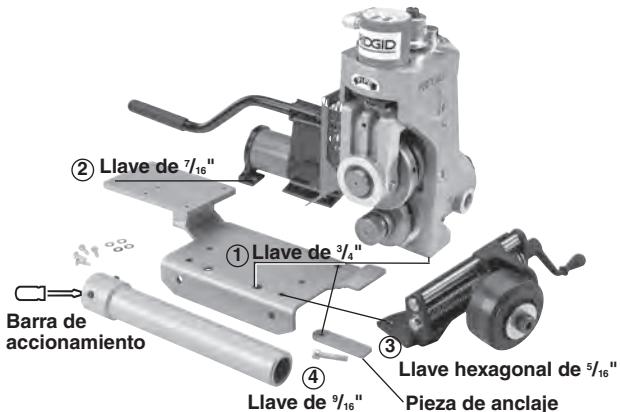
Montaje de la ranuradora 918 sobre la base de la roscadora Compact 300 o de la roscadora 1233
